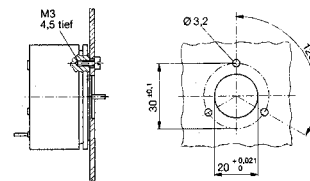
Bohrplan für Befestigung mit 3 Zylinderschrauben M3.
